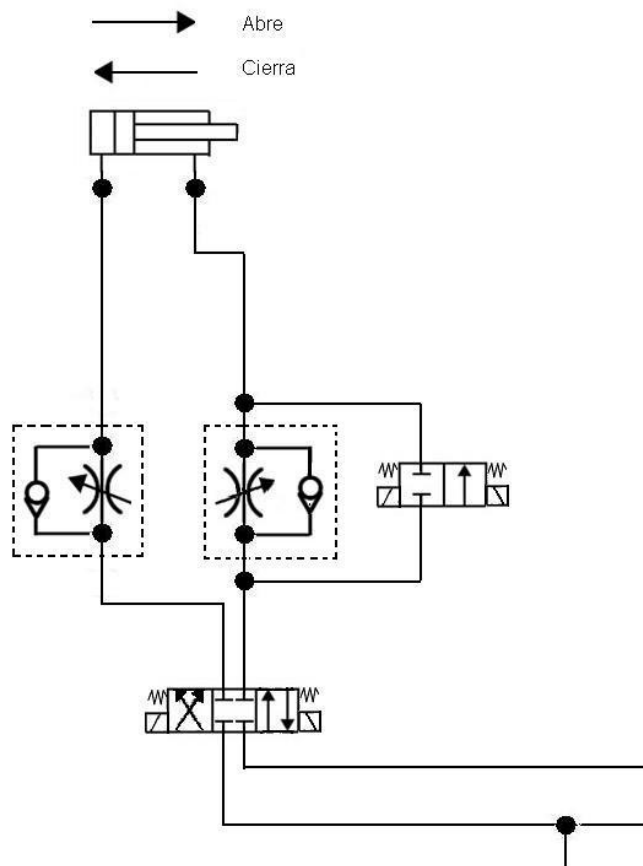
Conjunto hidráulico para la sección de acoplamiento del molde
